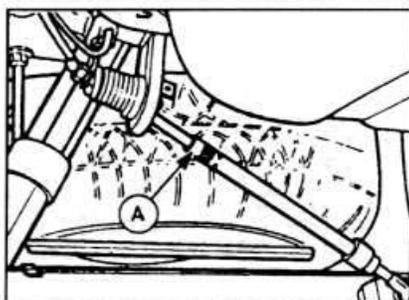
Расположение тяги регулятора давления. A - точка соединения трубы с резьбовым стержнем.
